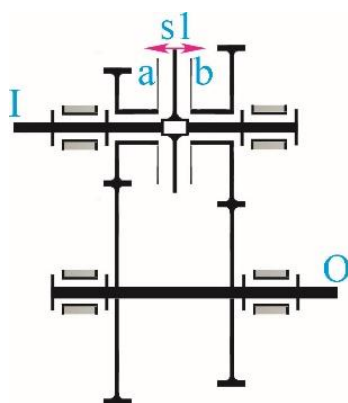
Кинематическая схема двухступенчатой коробки передач GB с неподвижными осями зубчатых колес и синхронизатором.
